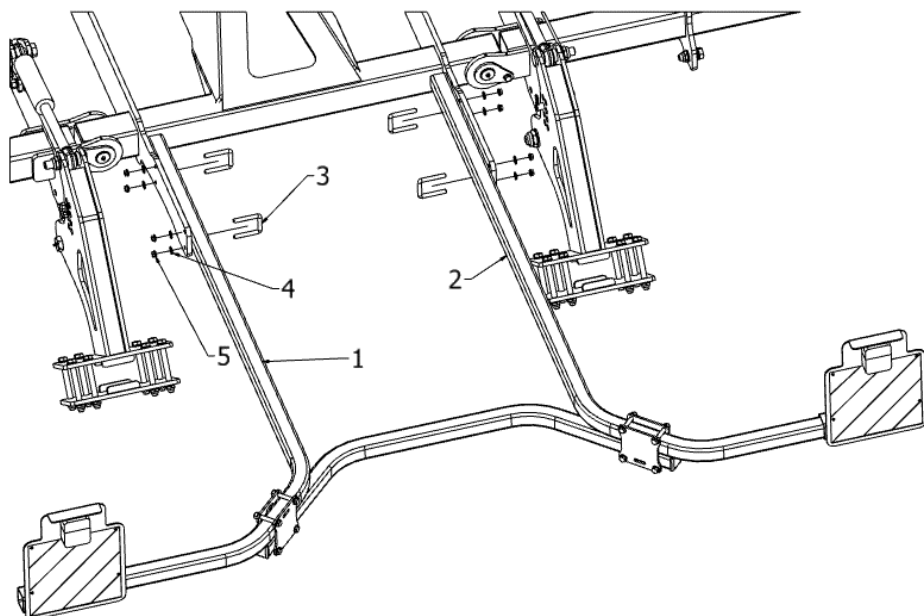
Befestigung der Beleuchtung am Maschinenrahmen.
